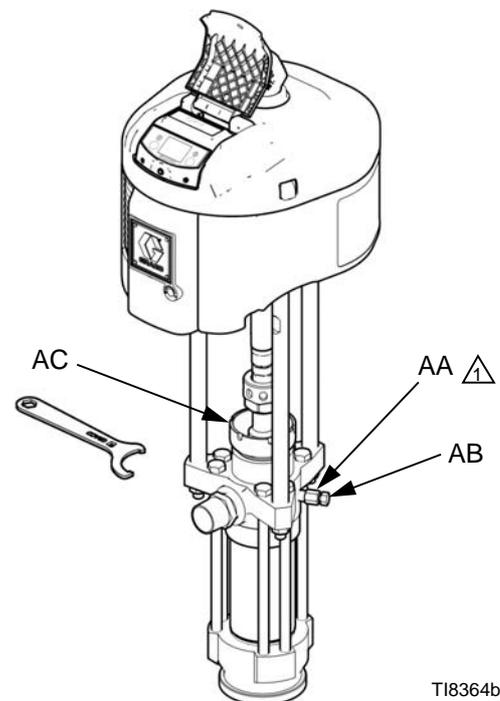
Vanne de purge et coupelle de presse-étoupe
